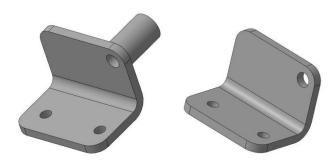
Изделие «Кронштейн поворотного механизма»
